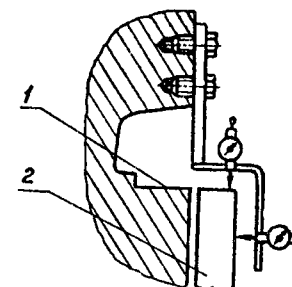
Приспособление для центровки валов электродвигателя и компрессора.
